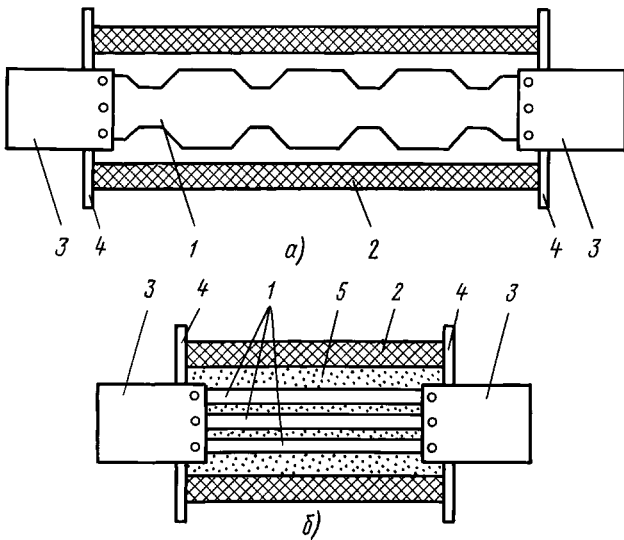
Примеры конструктивного исполнения предохранителей закрытого типа (а) и с наполнителем (б): 1 – плавкие вставки; 2 – изолирующий патрон (корпус); 3 – токопроводящие детали; 4 – защитные колпачки; 5 – наполнитель
